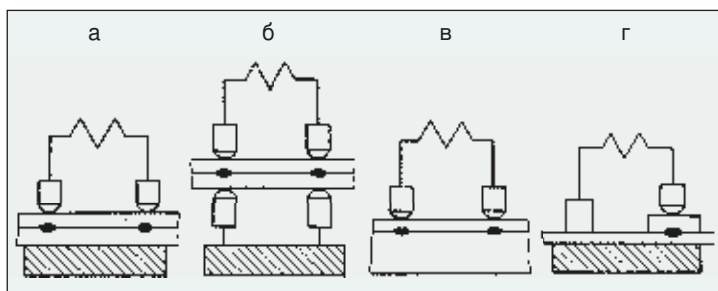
Схемы односторонней двухточечной сварки: а — сварка на токопроводящей подкладке; б — сварка с использованием замкнутых нижних электродов; в — сварка без токопроводящей подкладки; г — сварка с холостым электродом
